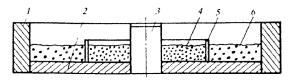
Схема прессования с применением гидроплиты: 1 кольно пресс-формы; 2 нижняя формовочная плита, 3 оправка; 4 формовочная смесь для упрочняющей середины круга; 5 проставка; 6 формовочная смесь для режушей части круга
